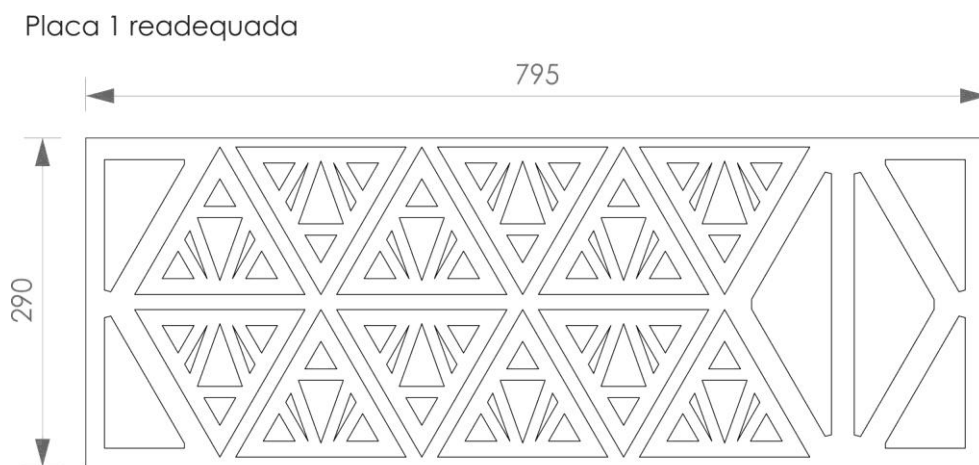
Desenho da placa prevista para outro modelo (dimensões em mm)
